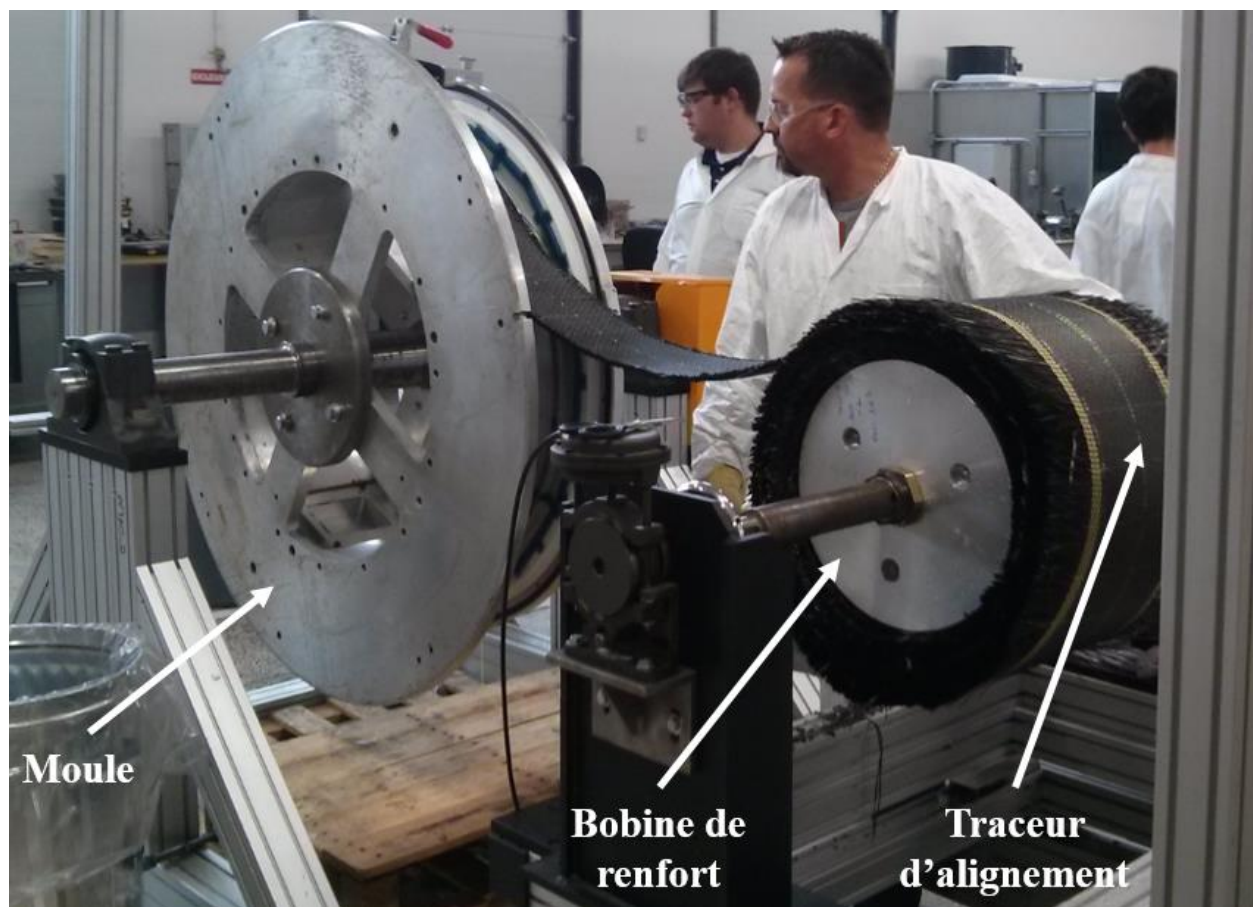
Machine d'enroulement du carter demi-échelle.
